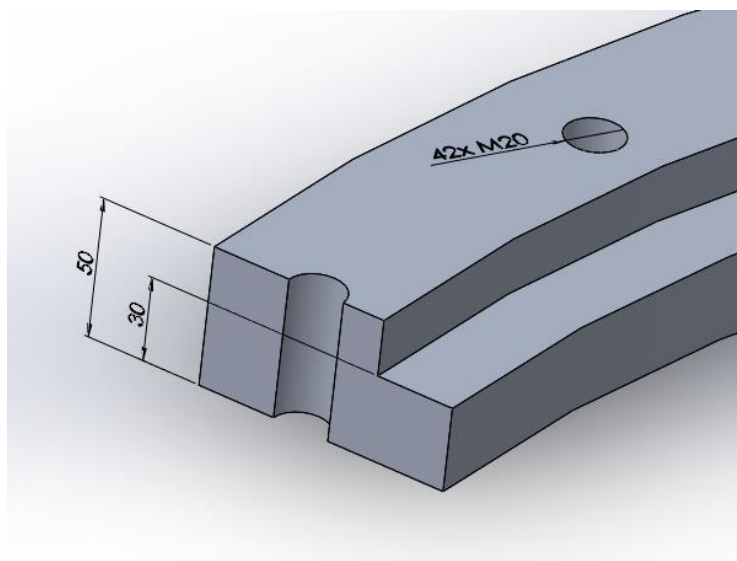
Dimensiones de la placa de apoyo del rodamiento.
